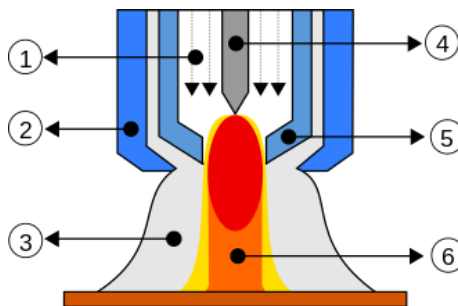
Esquema de soldadura TIG [1]
